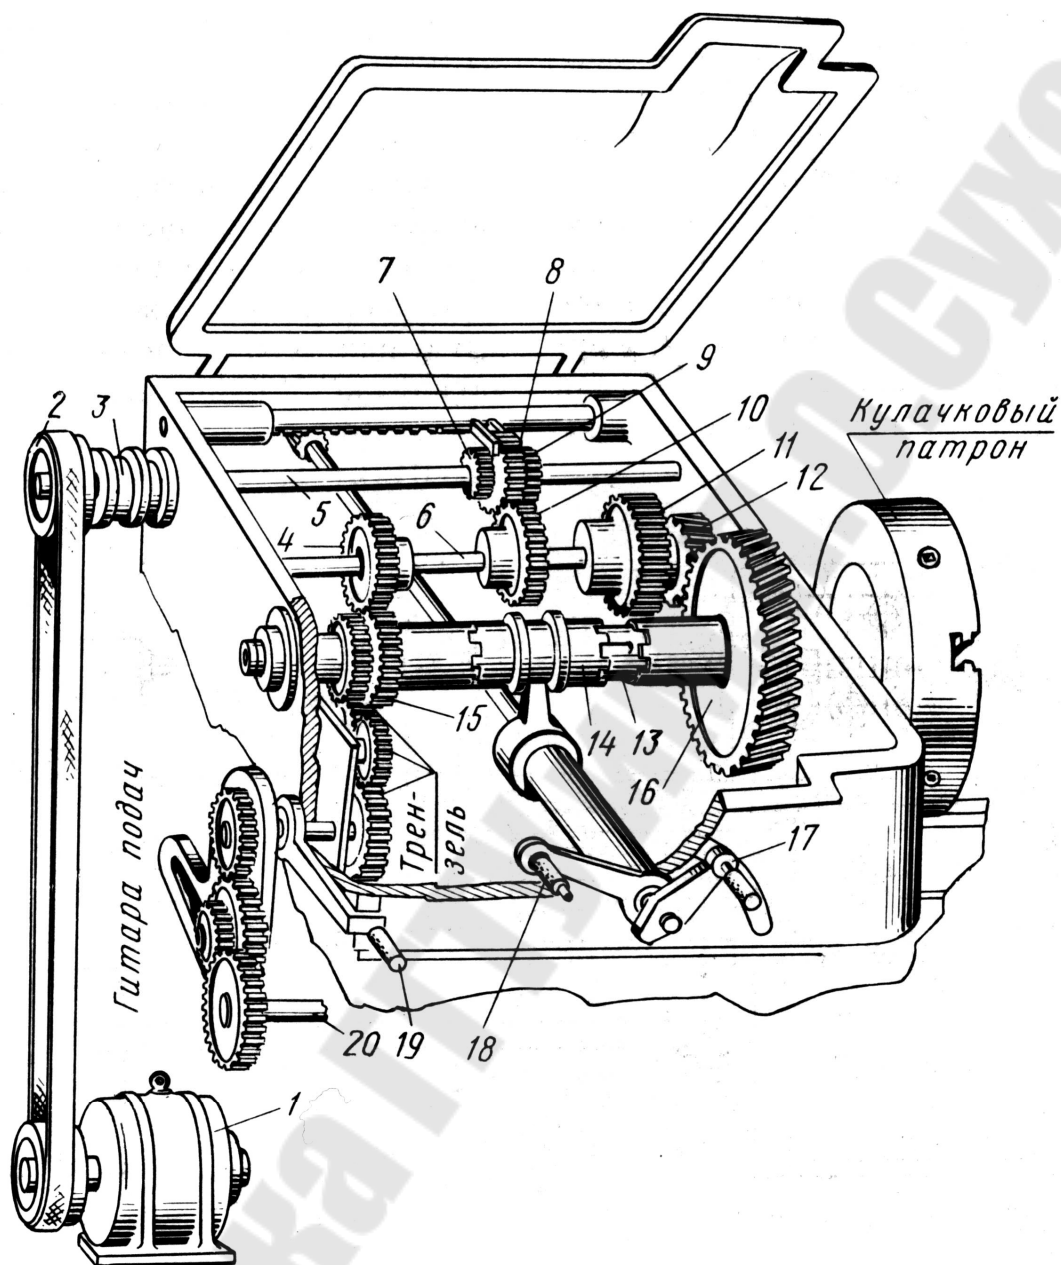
Механизм управления блоком зубчатых колес и муфтой с соосным расположением рукояток
